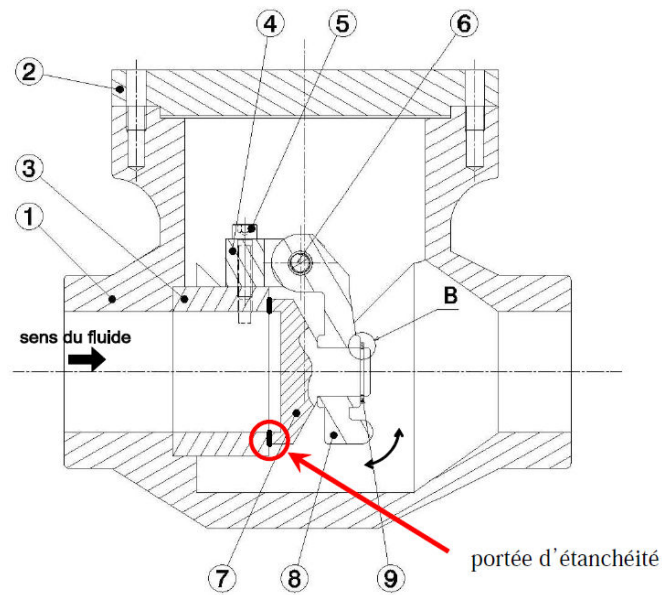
Plan d'un appareil de robinetterie (type : clapet sans retour)
